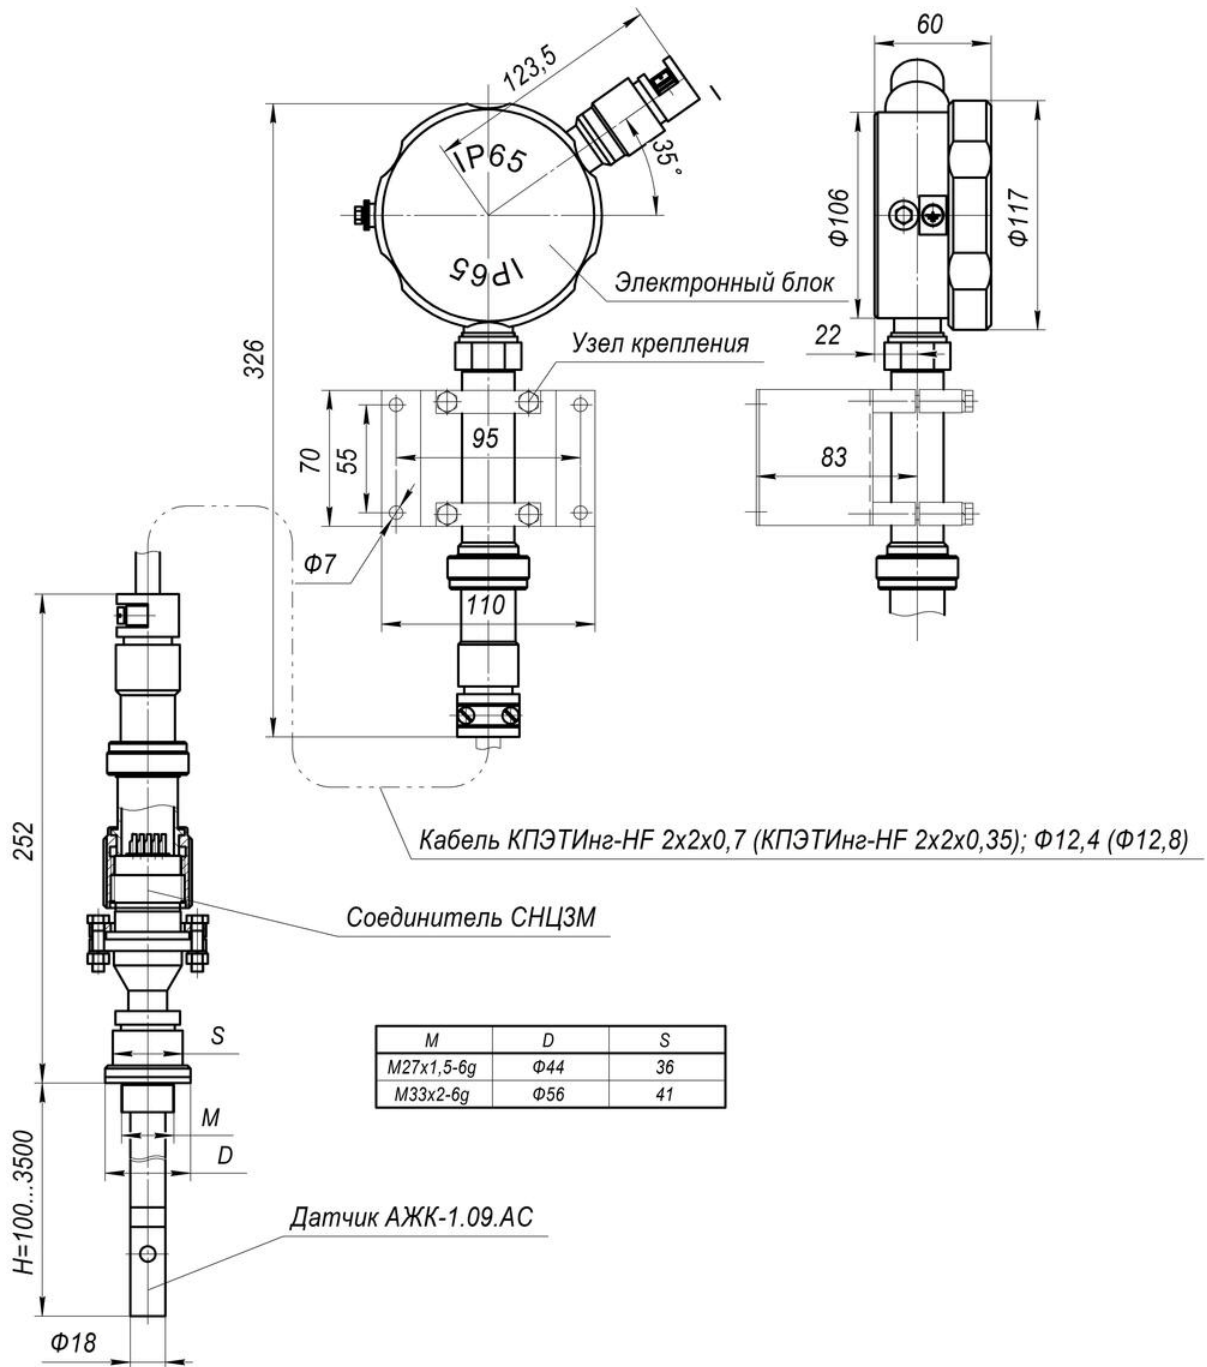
Габаритные, установочные и присоединительные размеры первичного преобразователя погружного типа с разнесенными электронным блоком и датчиком тип корпуса ПП - "Н" (нерж. сталь)
